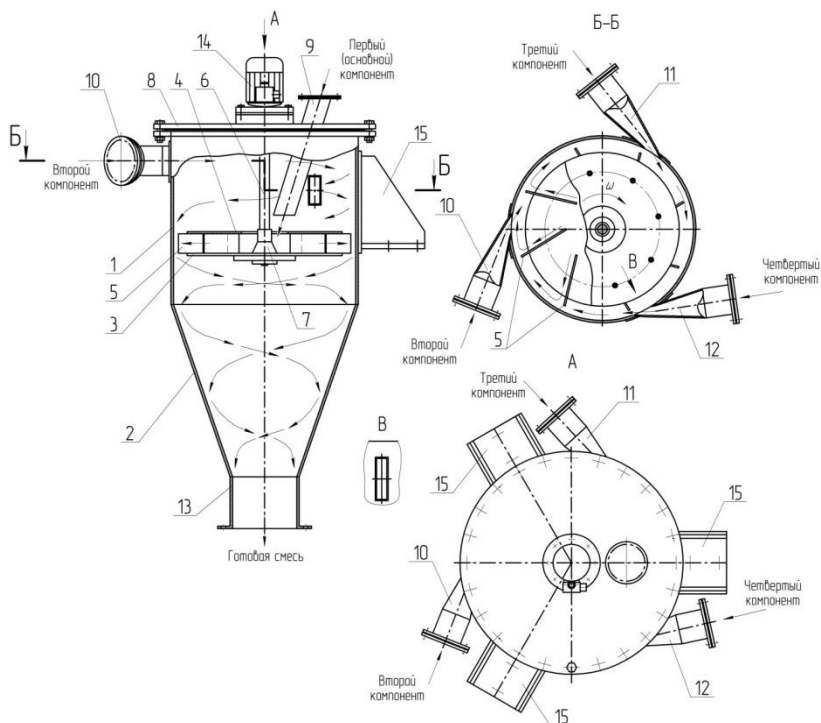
Роторно-центробежный смеситель со смещенными тангенциальными патрубками
